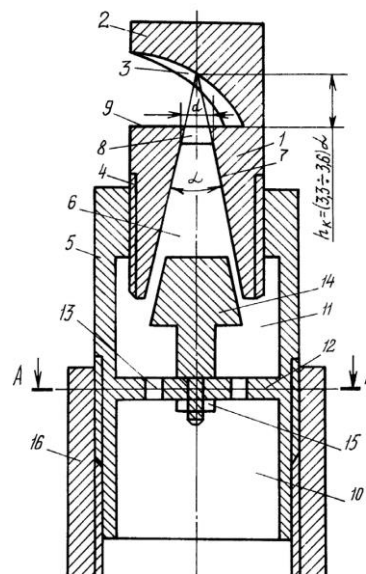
Схема дощоутворювального пристрою дощувальної машини: 1 – секторний розпилювач; 2 – дефлектор; 3 – відбивна поверхня; 4 – різьба; 5 – дросель; 6 – прохідний канал; 7 – конфузور; 8 – калібрований циліндричний отвір; 9 – площа витікання; 10 – входна камера корпусу; 11 – вихідна камера корпусу; 12 – перегородка; 13 – отвори; 14 – усічений конус; 15 – гайка; 16 – штуцер.
